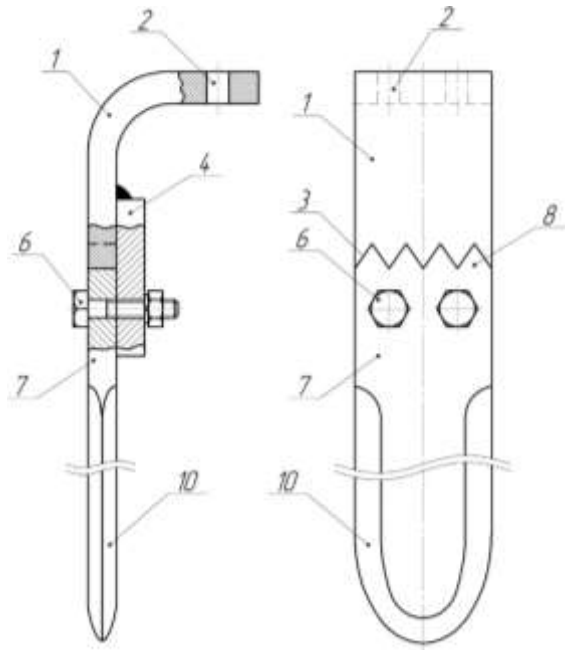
Схема рабочий орган почвообрабатывающей фрезы.
